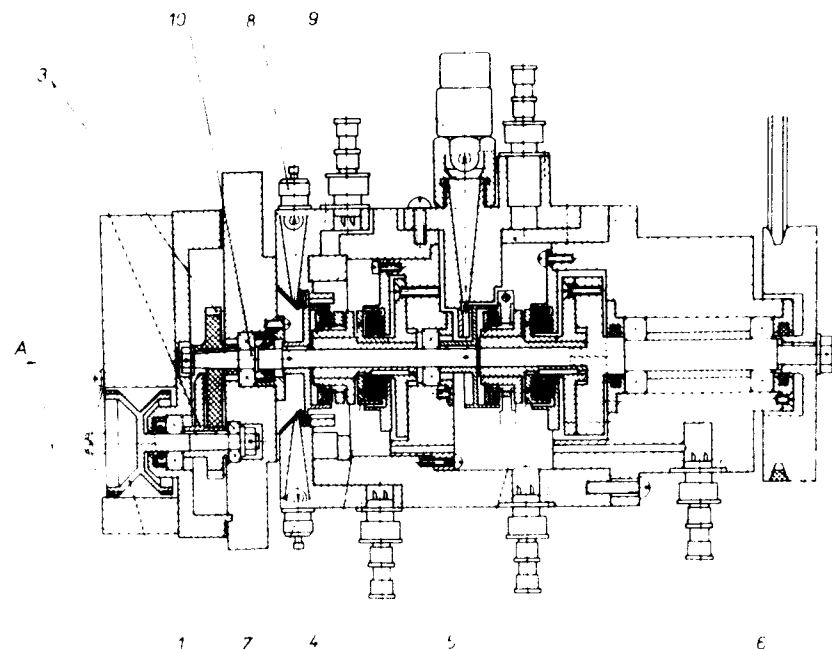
Лентопротяжный механизм. 1 - обрешиненный барабан, 3 - безударный однооборотный механизм с остановкой, 4 - тормозная быстродействующая электромагнитная фрикционная муфта, 5 - приводная быстродействующая электромагнитная фрикционная муфта, 6 - приводной шкив, 7-9 - фотодатчики управления и контроля рабочего цикла фоторегистратора, 10 - вал.
